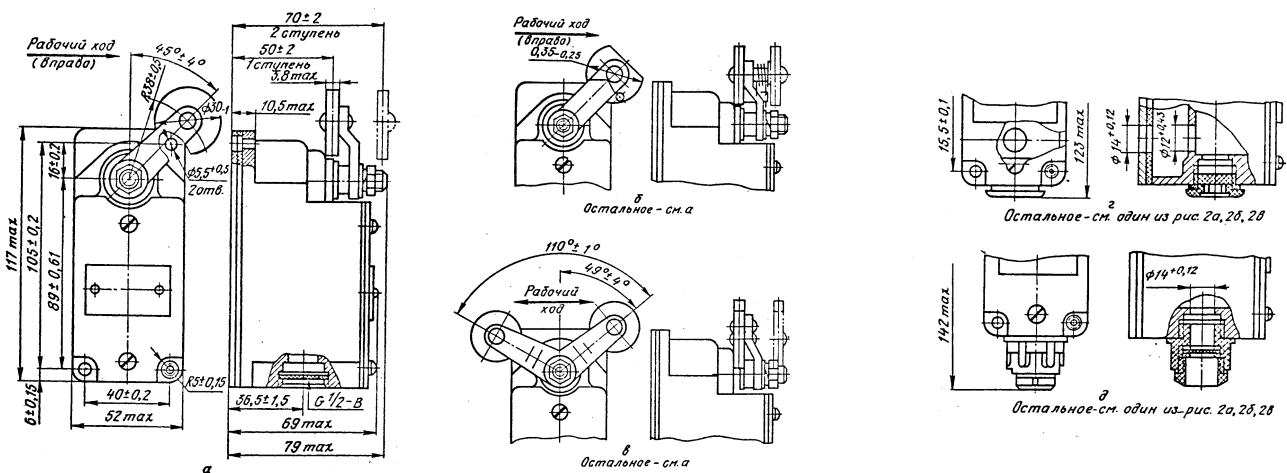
Габаритные, установочные и присоединительные размеры выключателей
